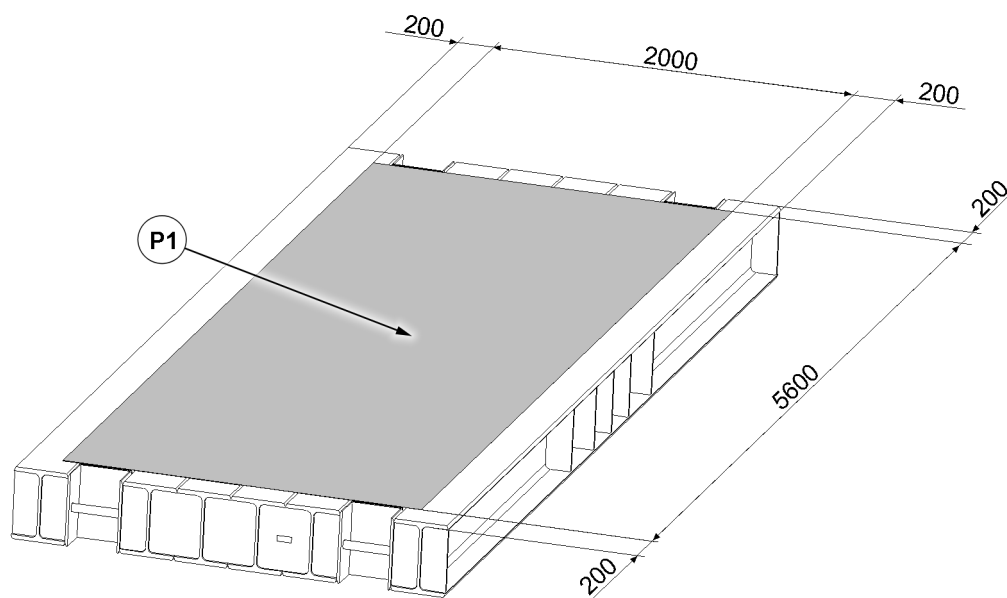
Superficie de apoyo permitida para placas de apoyo
